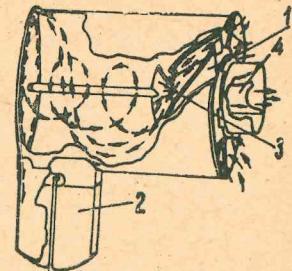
Центробежный воздухоочиститель [с неподвижными лопатками
